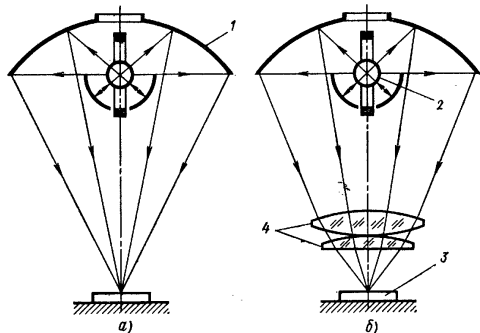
Оптические схемы установок для сварки лучистой энергией:
